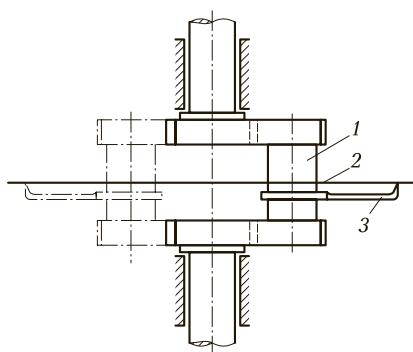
Приспособление для контроля перпендикулярности осей шатунных шеек коленчатого вала и оси цилиндра:
